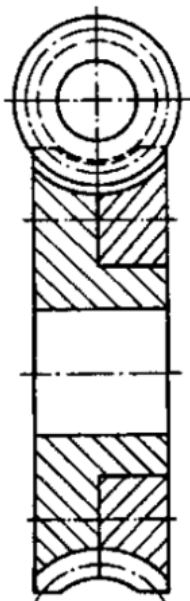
Getriebe mit geteiltem Schneckenrad (Henschel Antriebstechnik, 1991)
